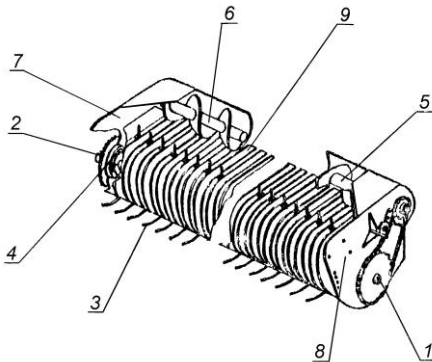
Подборщик: 1 – приводной вал; 2 – предохранительная муфта; 3 – пружинные зубья; 4 – направляющая дорожка; 5 – левый шнек; 6 – правый шнек; 7 и 8 – боковины; 9 – скат.
